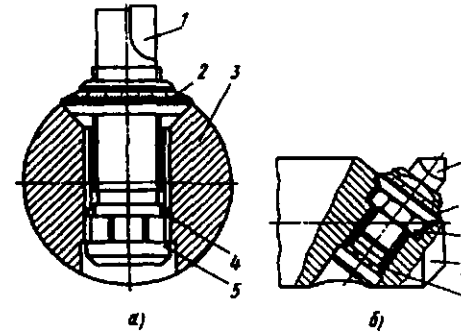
Схемы закрепления резцов в расточной борштанге с точным регулированием на размер
